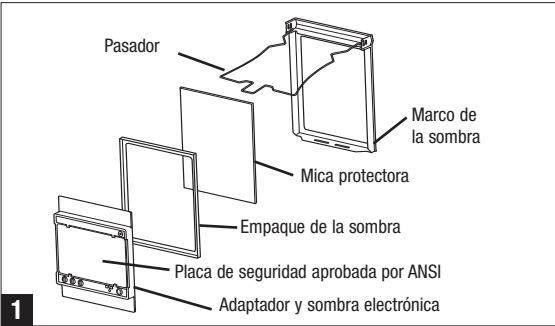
El lugar del lente se encuentra en el marco de lente localizado en el protector de soldadura.
